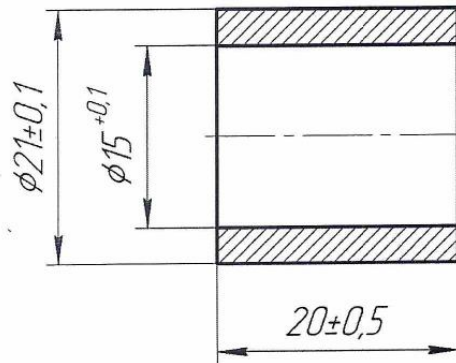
Цилиндрический образец для испытаний на стойкость к солеотложению
